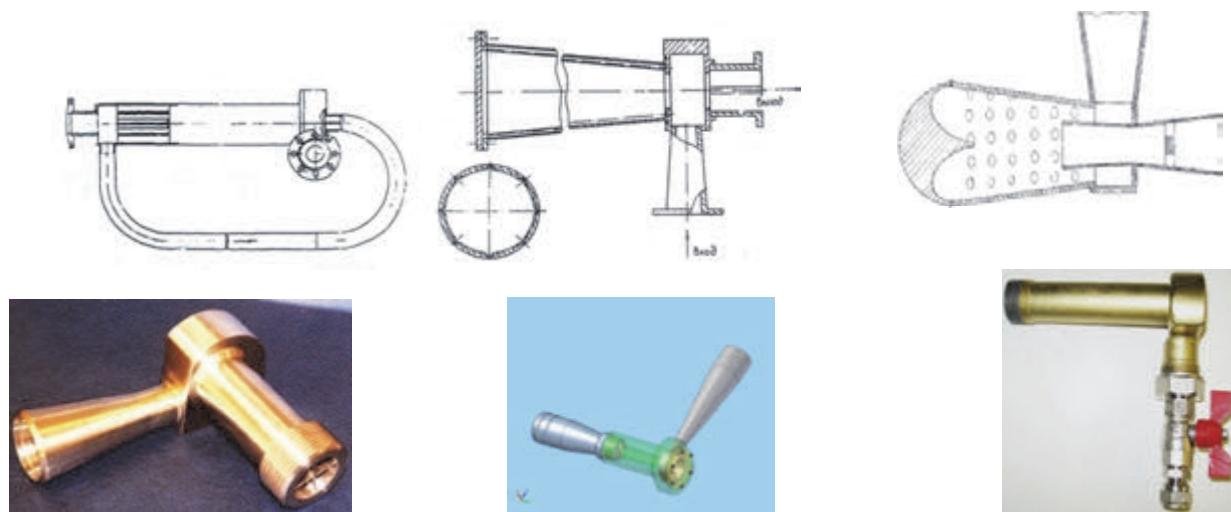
Вихревой гидрокавитатор – варианты конструктивных схем и конструкций
